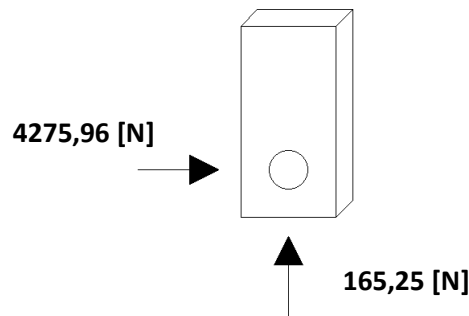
Fuerzas que actúan en cada par de plaquetas que unen los dos chasis.
